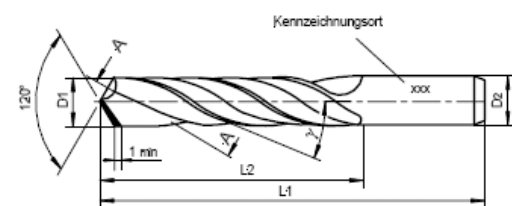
VHM-Werkzeug – Spiralbohrer mit eingelöteten oder eingesinterten PKD-Schneiden
